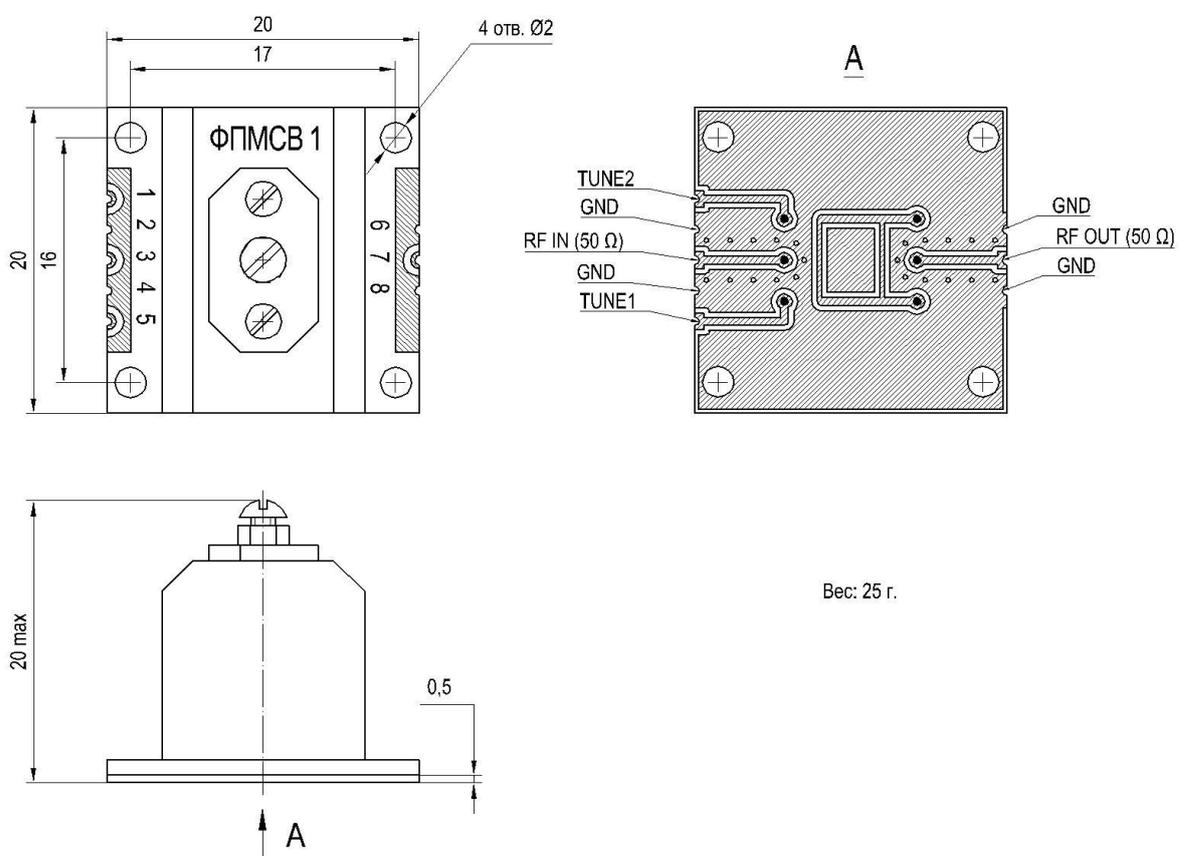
Габаритные и присоединительные размеры, обозначение выводов полученных образцов ППФ на МСВ для поверхностного монтажа
